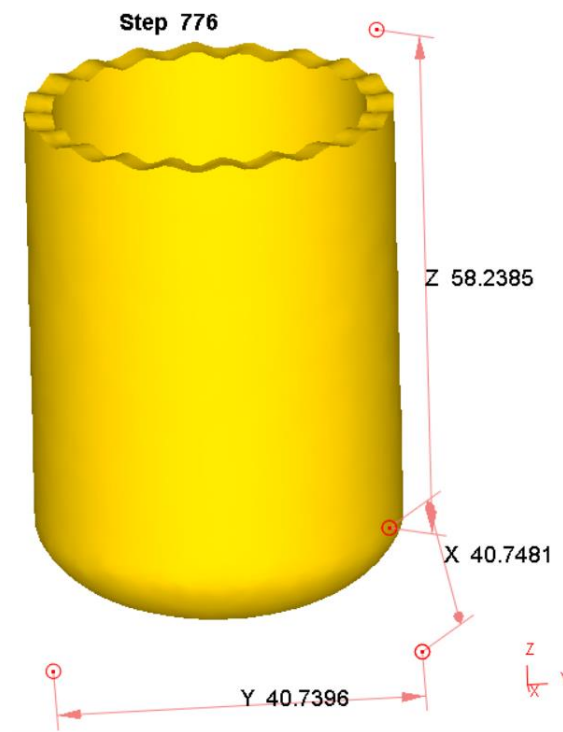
Форма та розміри заготовки після витягування з розрахованого об'єму
